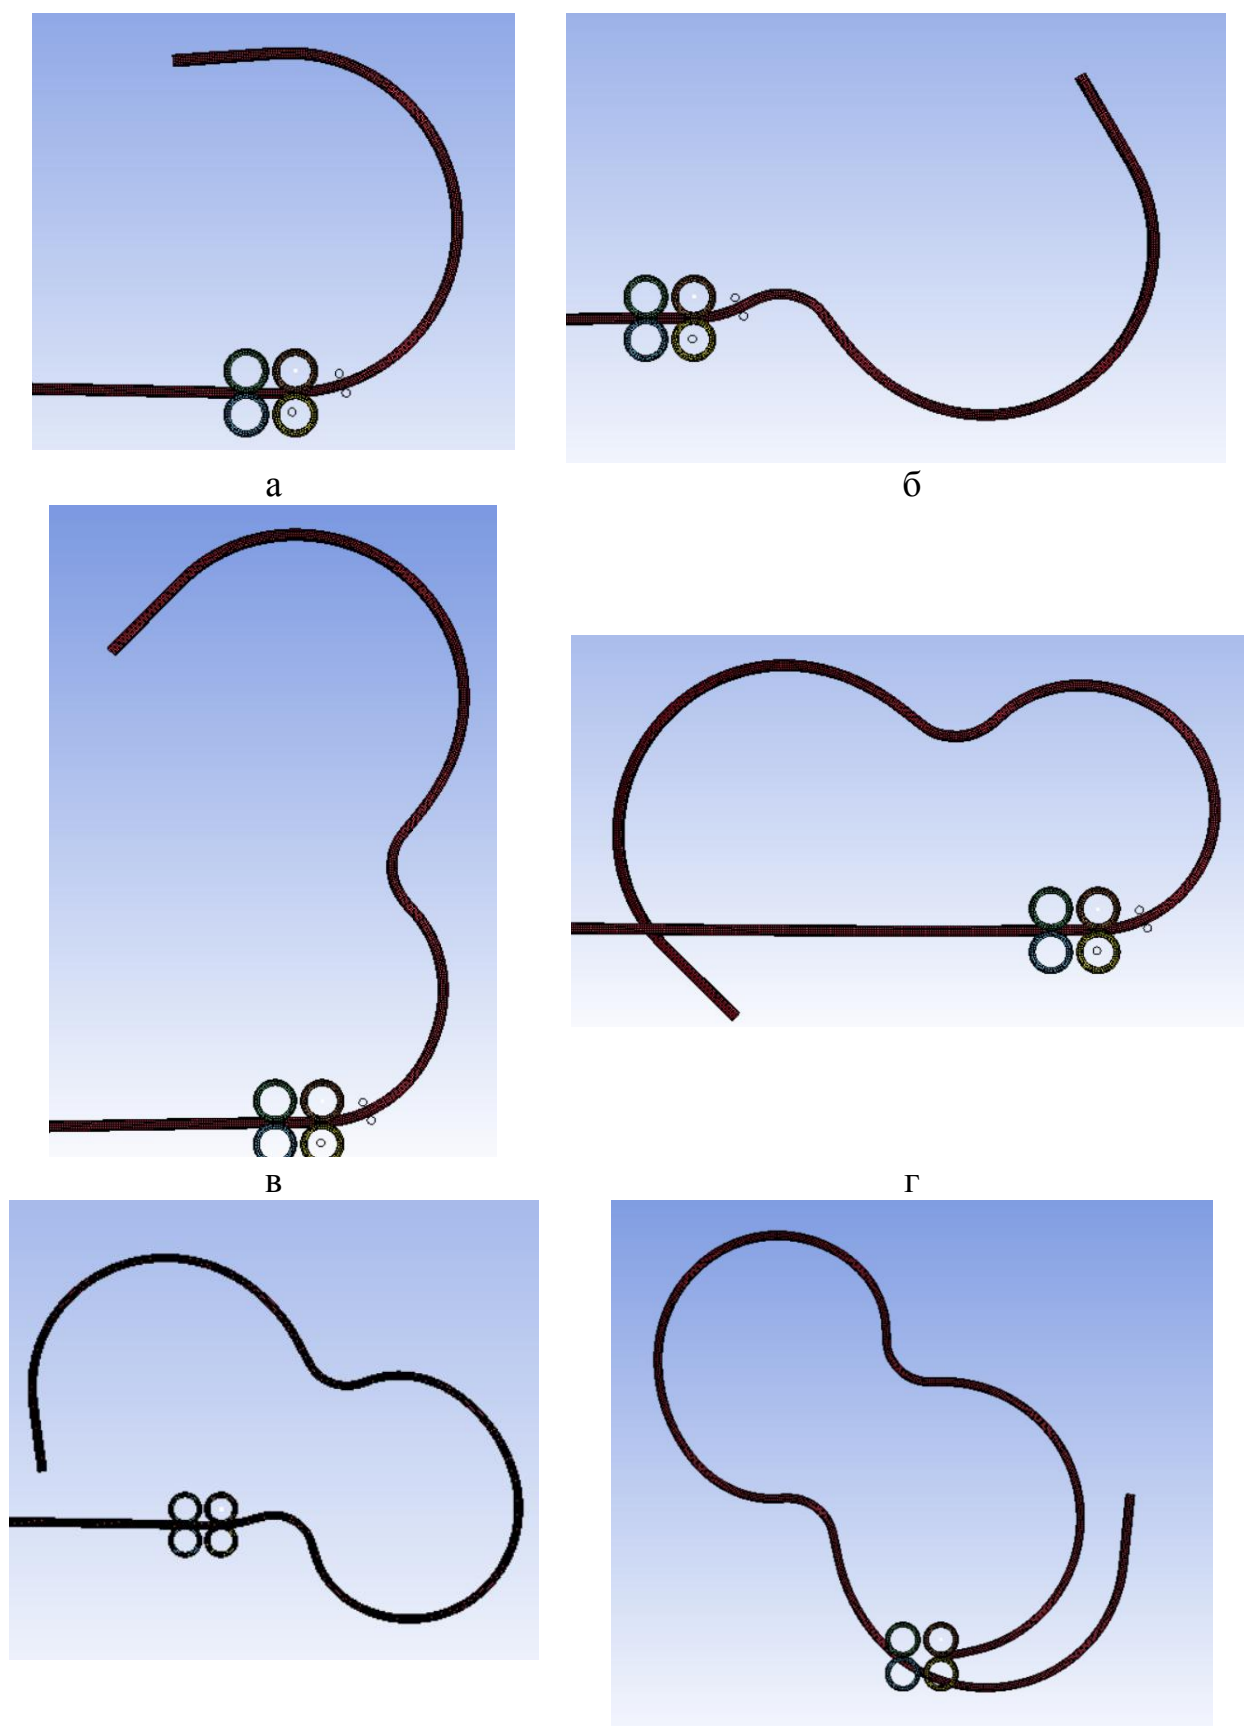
Этапы гибки заготовки для изготовления детали «Восьмерка»
